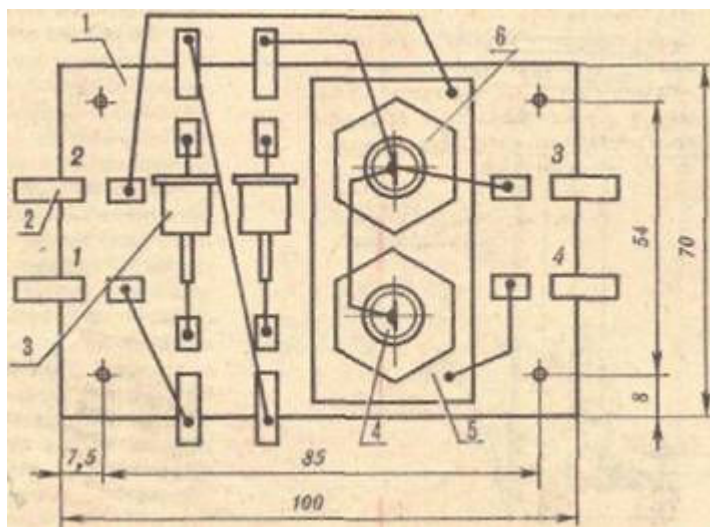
Монтажная схема приставки: 1 — плата, 2 — лепесток, 3 — диод, 4 — конденсатор К50-12, 5 — контактная пластина, 6 — гайка.
